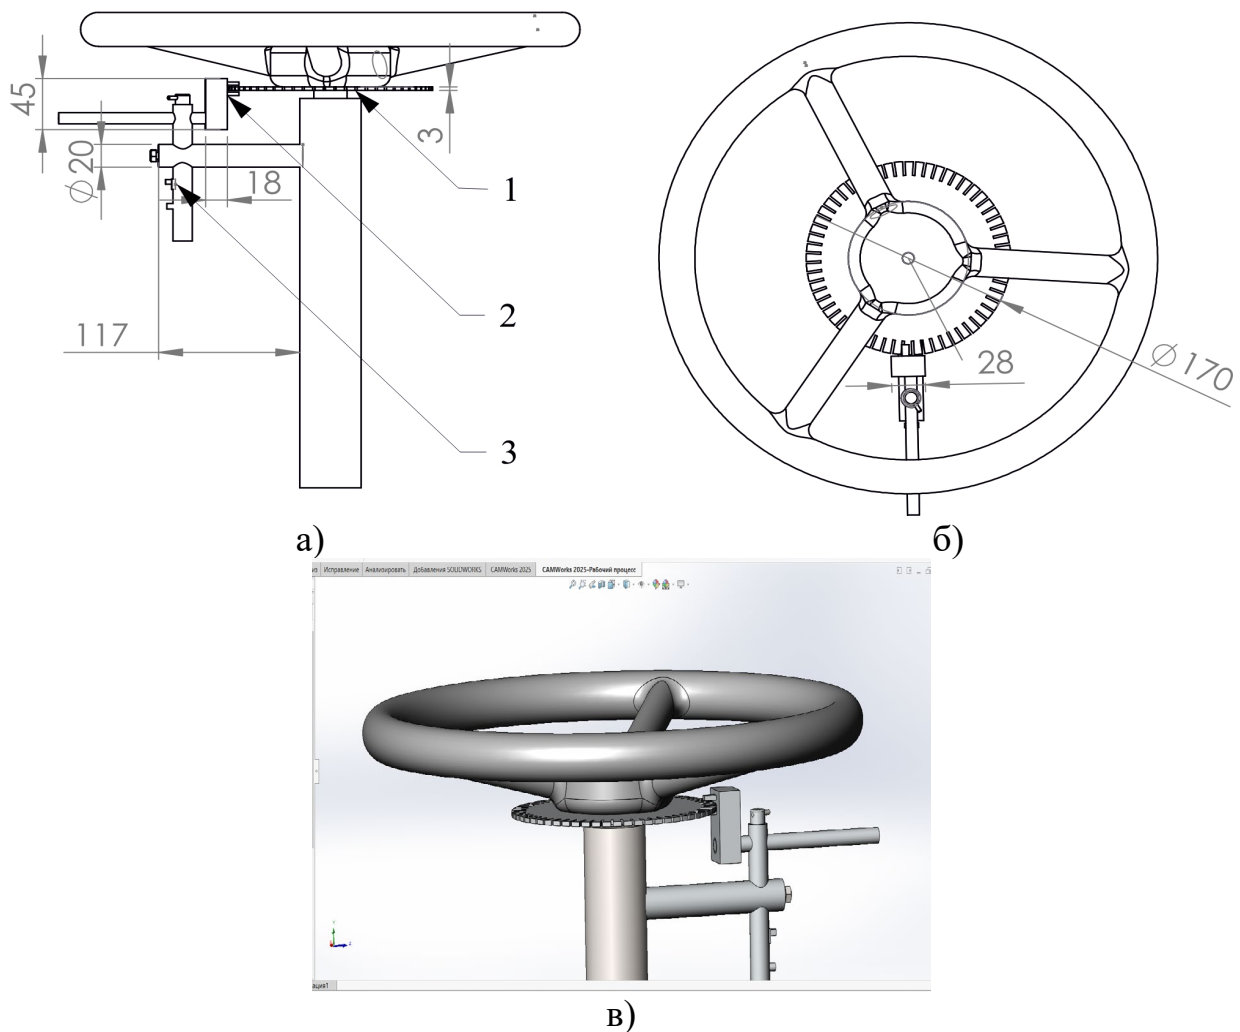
Пристрій для визначення кутового прискорення рульового колеса:
